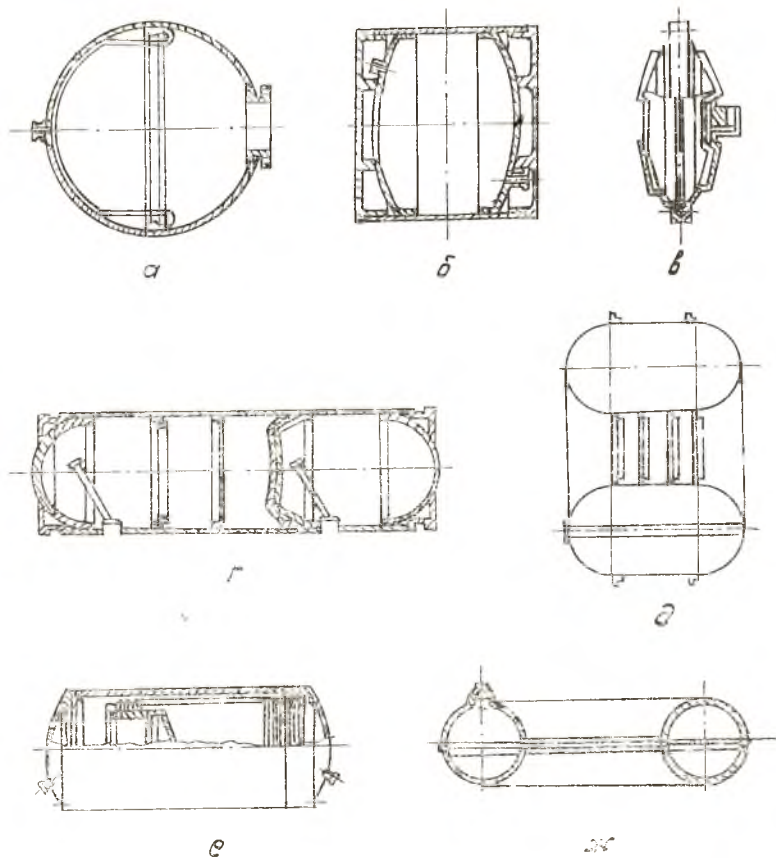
Типы баков: а — сферический бак с вытеснителем; б — цилиндрический бак; в — чечевицеобразный бак; г — блок цилиндрических баков, д — торовый цилиндрический бак; е — бак с силонным вытеснителем; ж — торовый сферический бак
